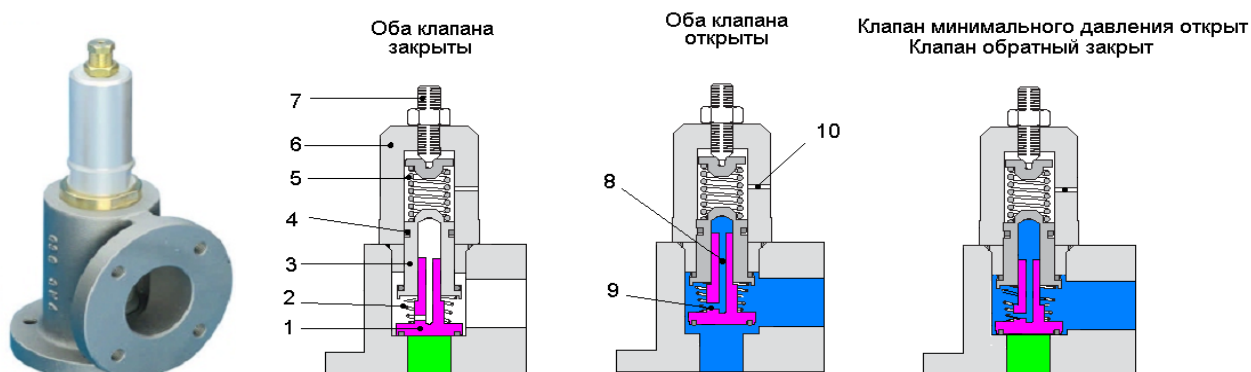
Клапан минимального давления типа G50: 1 – тарелка обратного клапана; 2 – пружина обратного клапана; 3 – поршень клапана минимального давления; 4 – кольцо уплотнительное; 5 – пружина клапана минимального давления; 6 – корпус (цилиндр поршня); 7 – винт регулировочный; 8 – канал осевой; 9 – канал радиальный; 10 – отверстие дренажное.
